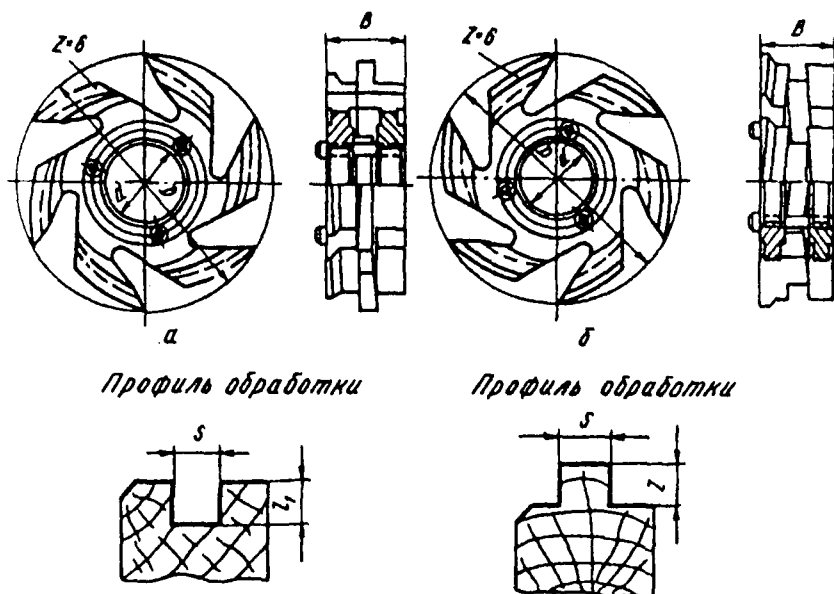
Фрезы для обработки пазов и гребней соединения К-4:
